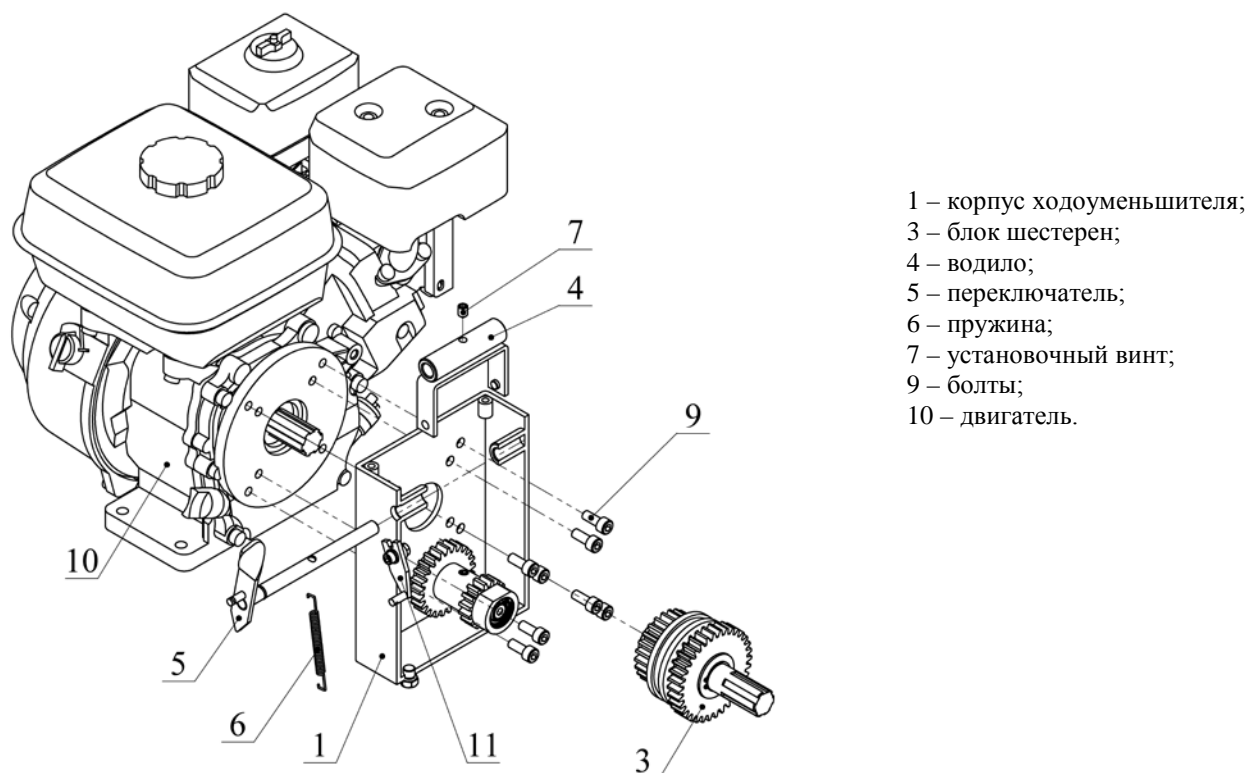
Схема установки ходоуменьшителя на двигатель мотоблока
